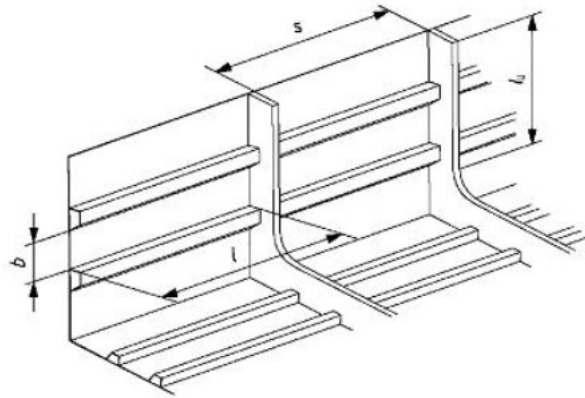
Croquis explicatorio de las dimensiones. Fuente: ISO 12215-5:2019
